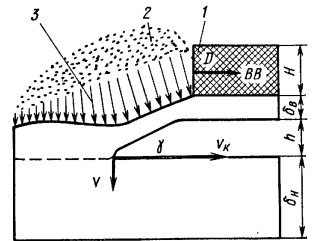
Схема сварки взрывом параллельно расположенных пластин:
